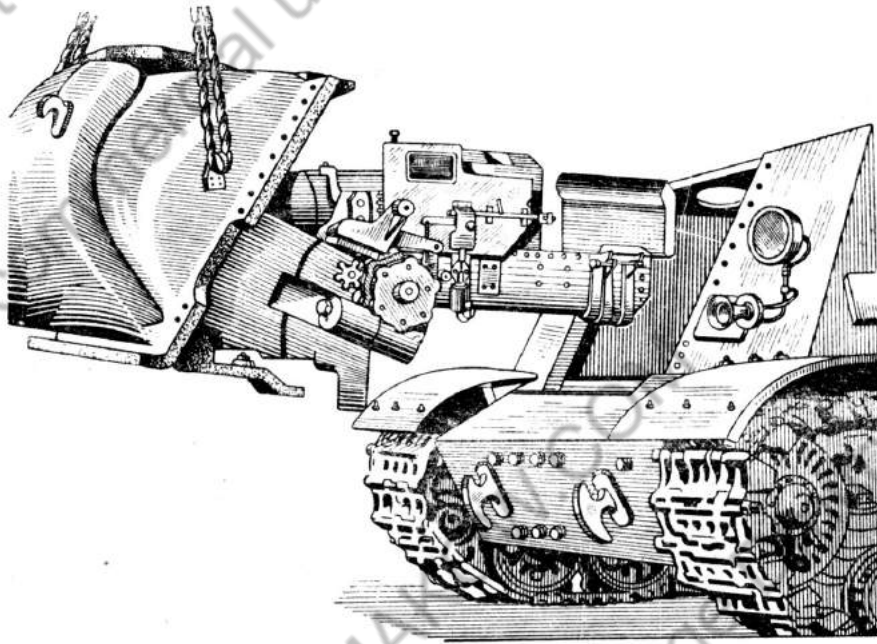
Вынимание орудия из корпуса самоходно-артиллерийской установки вместе с неподвижной и подвижной бронировками
